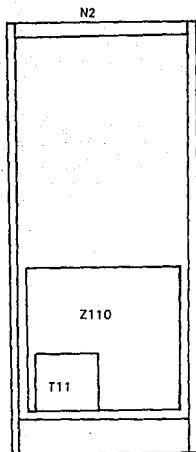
SECCION Z110 DEL ADITAMENTO PLANIGRAFICO.
